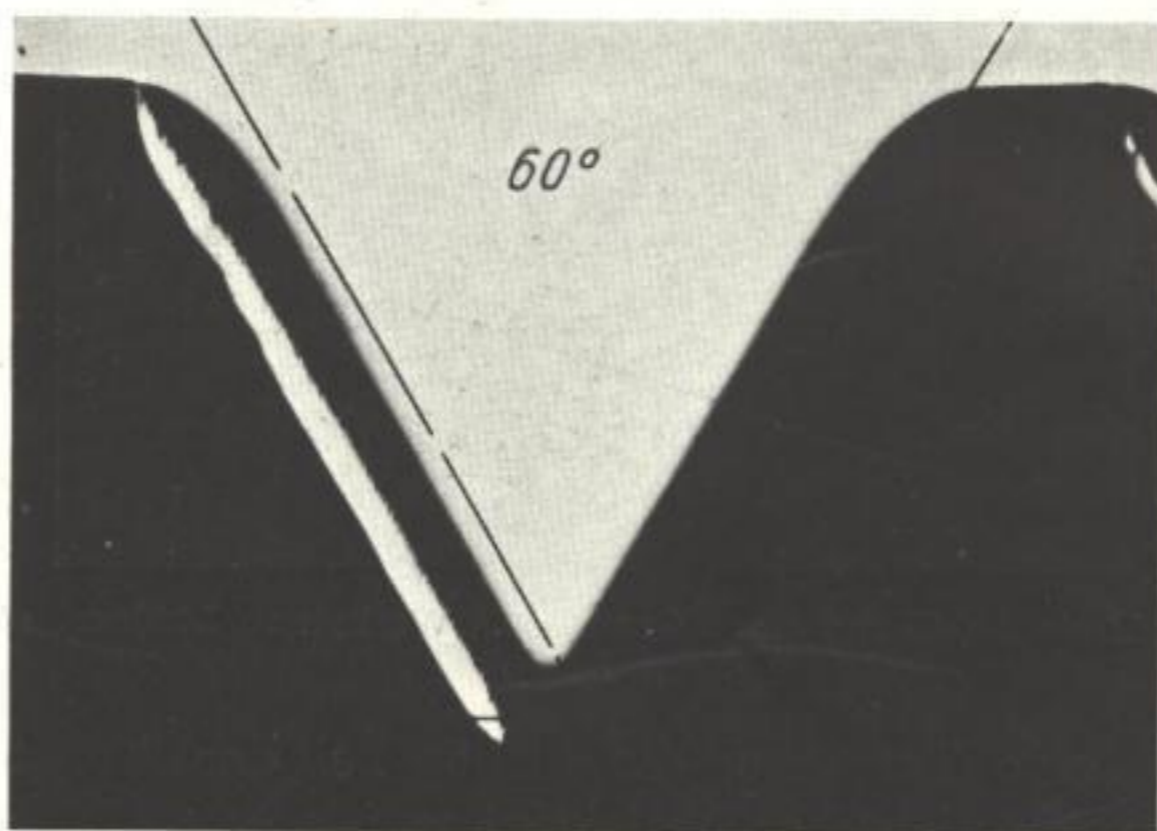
Fehlerhafte Abbildung eines Gewindes durch falsche Beleuchtung.
